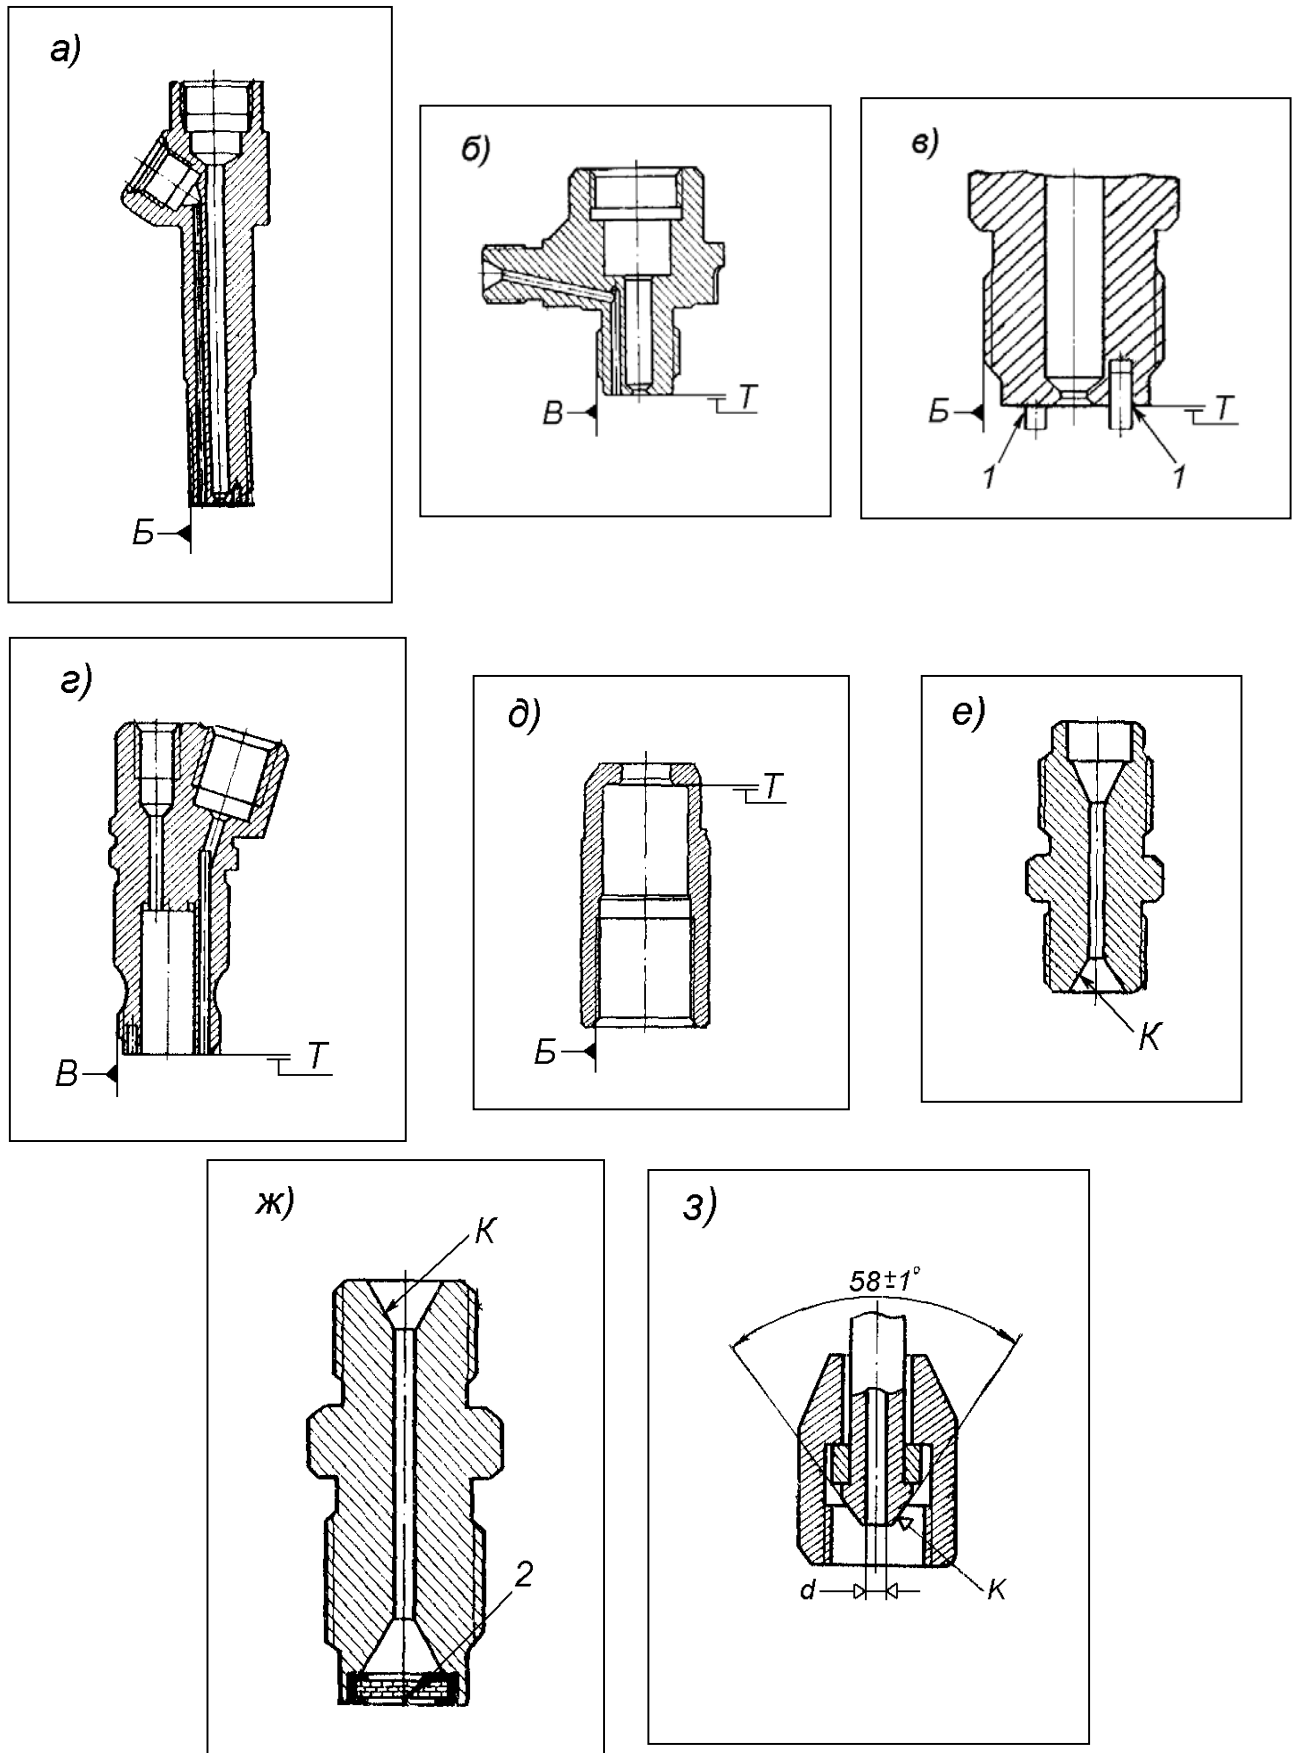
К контролю СЧ форсунок корпуса форсунки: а), б) – мод. 16; в) – мод. 26, 261, 262, 263, 181; г) – мод. 33, 19, 191; д) – гайки корпуса; е), ж) – штуцеров; з) – топливопровода высокого давления. Биение торца "Т" на диаметре относительно поверхности "Б" допускается не более 0,05 мм;  $d=2,0\pm 0,15$  мм – сужение канала в зонах высадки конусов не допускается.
